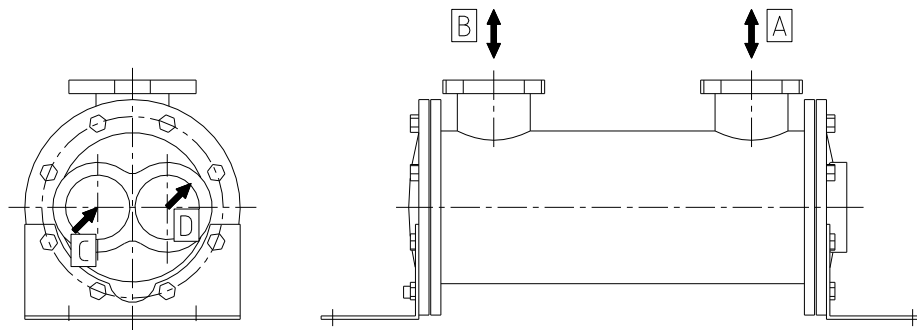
Öl-/Wasserkühler Ausf. TAK „2-Wege“
